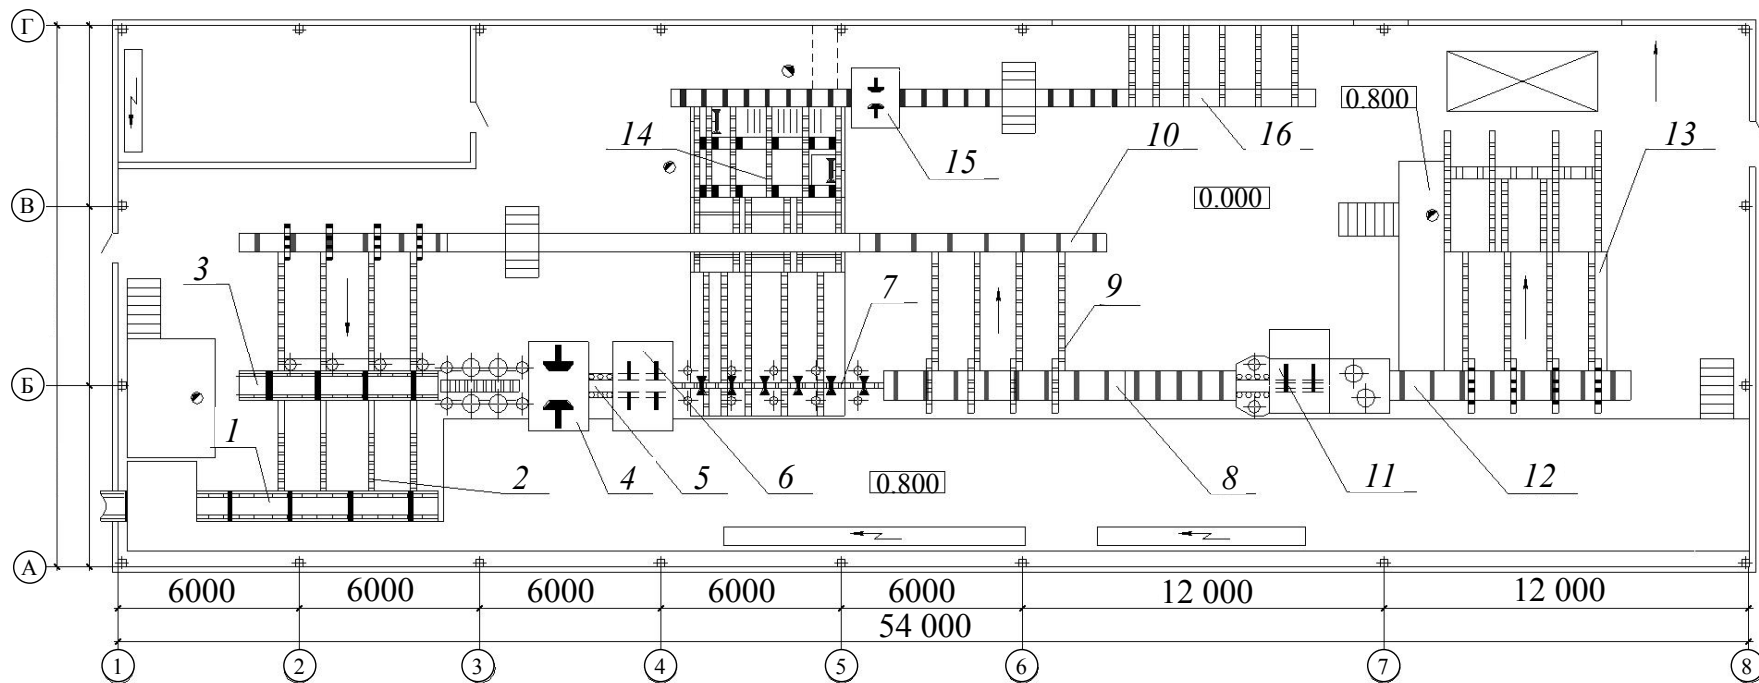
Схема лесопильного цеха на базе фрезернопильного оборудования:
